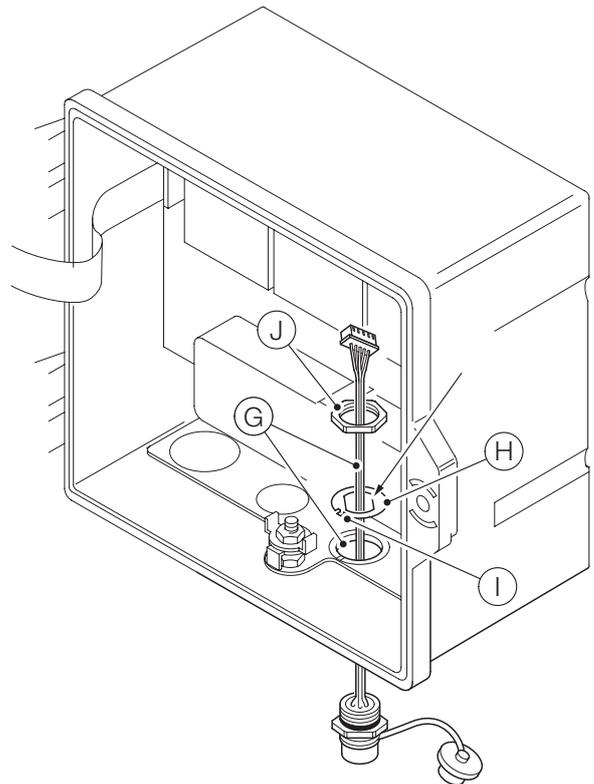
Подготовка креплений соединительного кабеля EZLink
